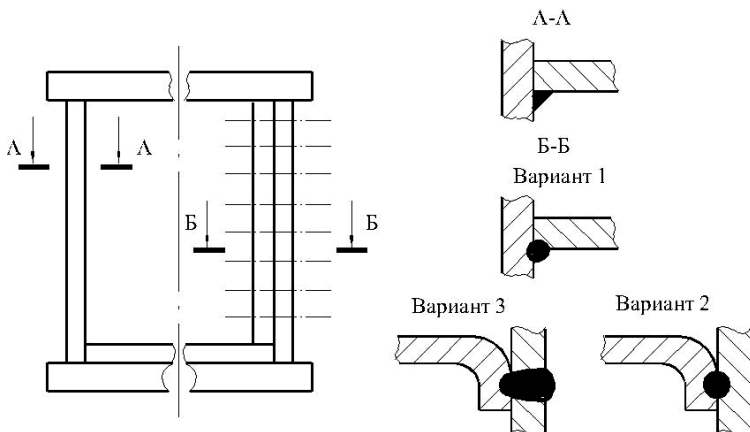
Типы сварных соединений диафрагм со стенками балок
